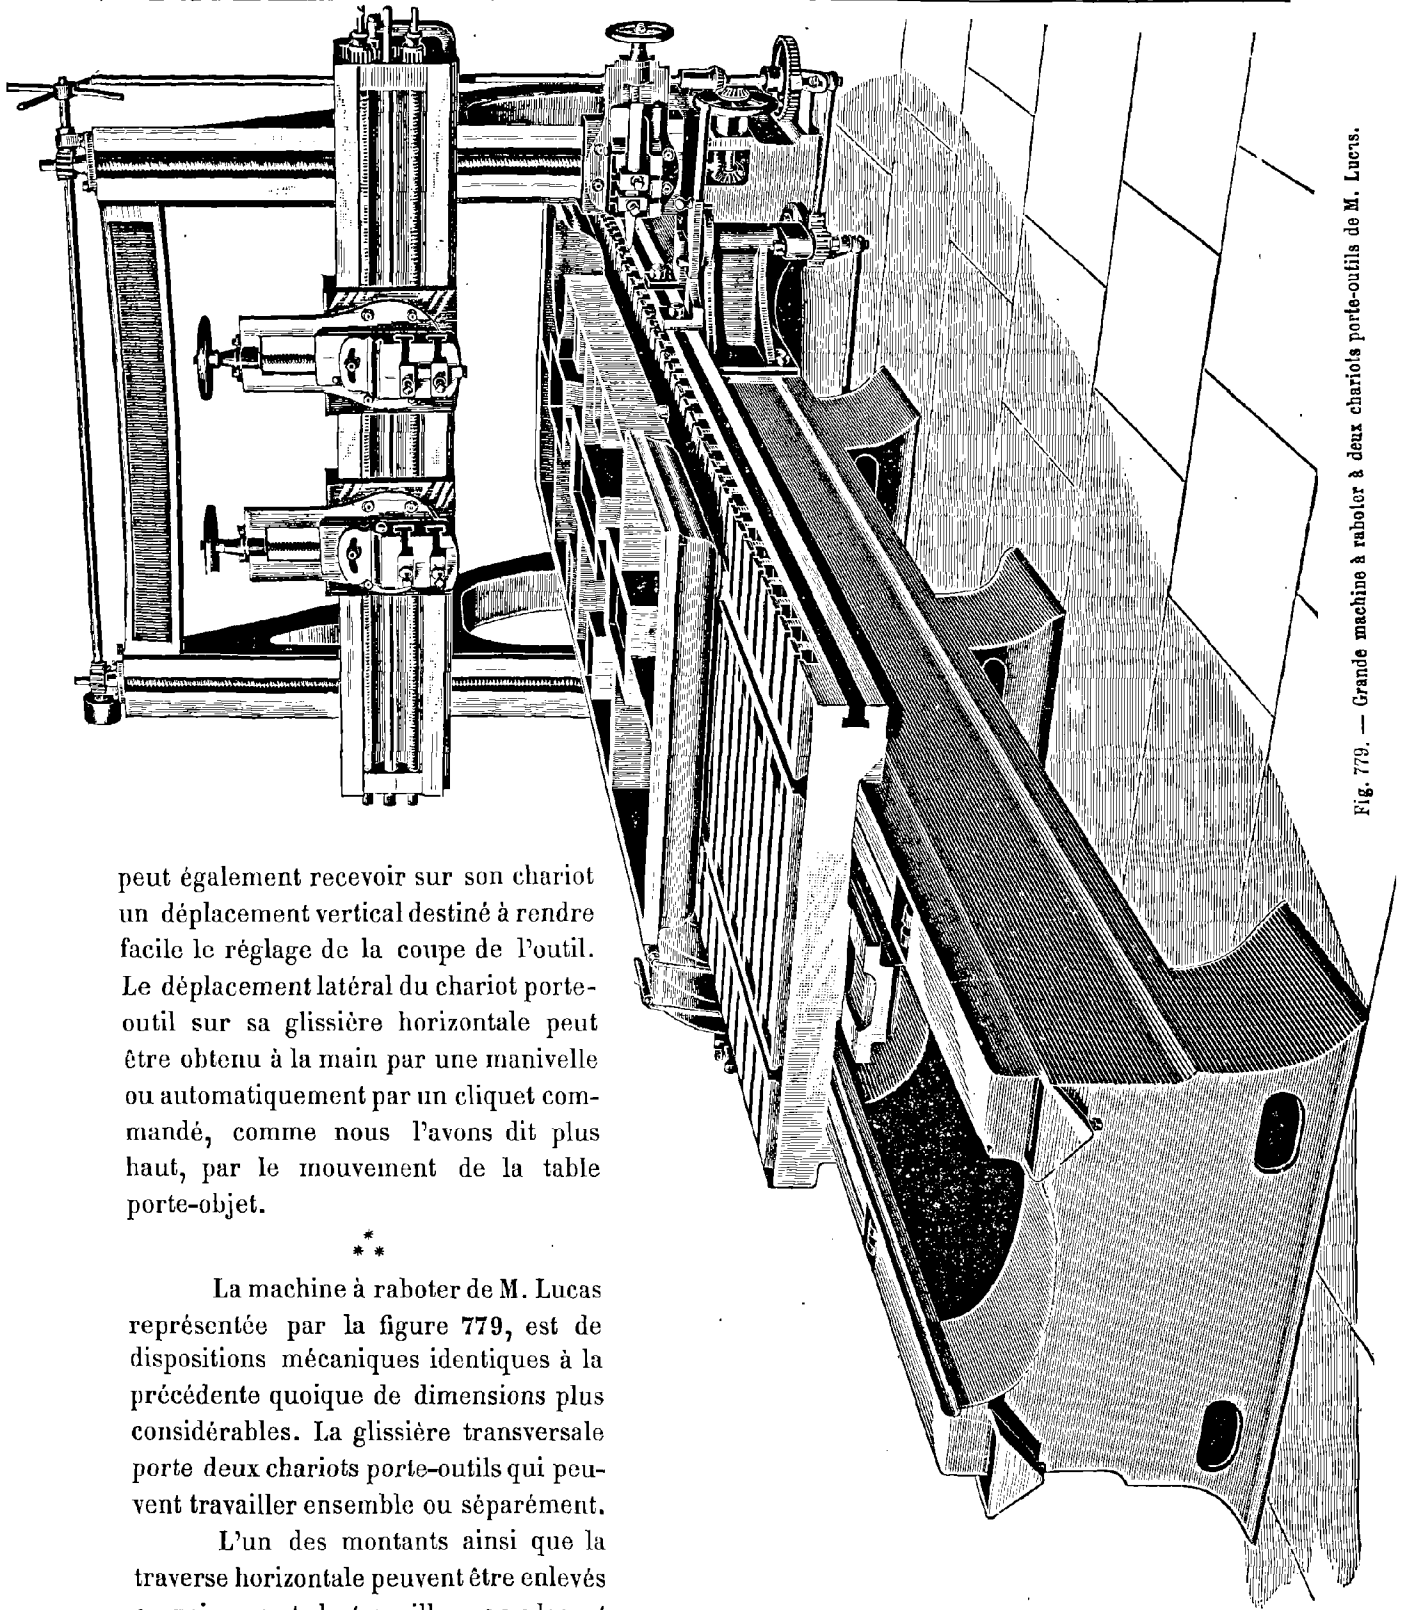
Grande machine à raboter à deux chariots porte-outils de M. Lucas.
